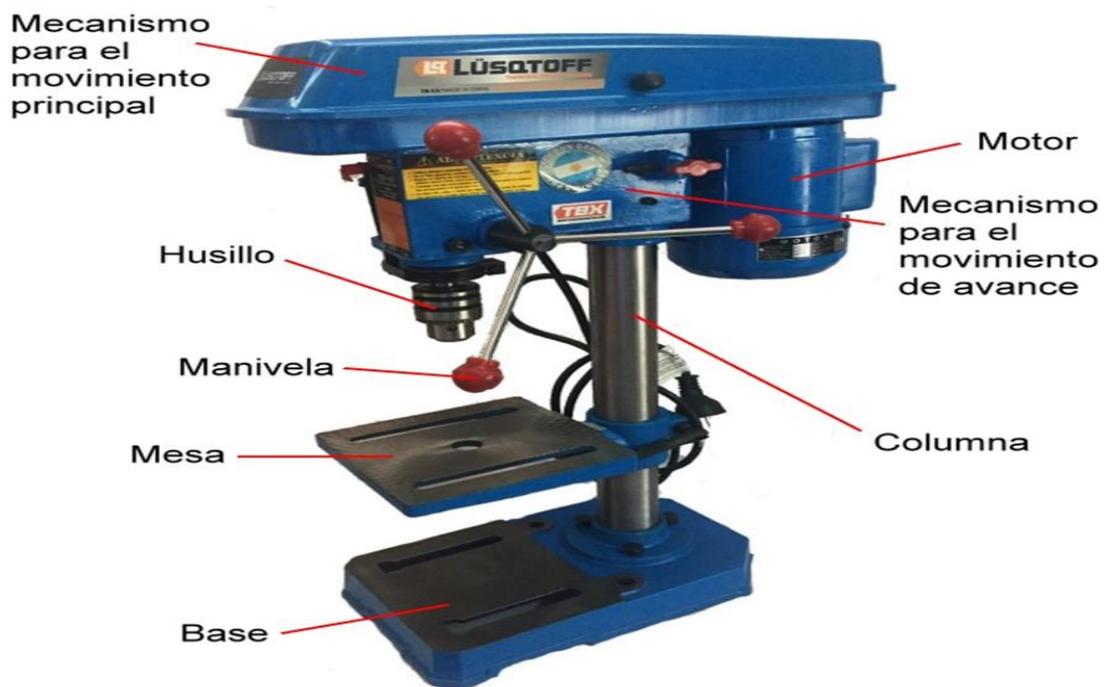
Partes de un taladro (De maquinas y Herramientas, 2018)
